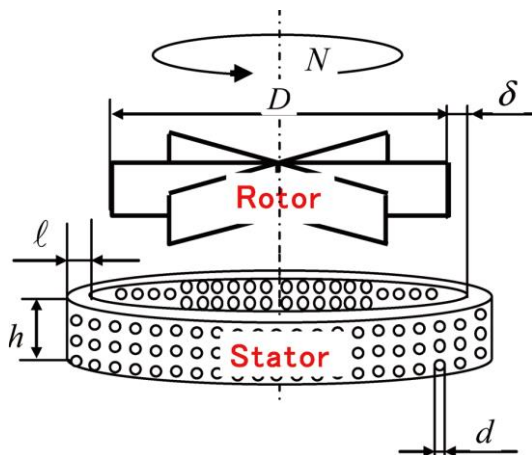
Dimensões do rotor e estator (retirado de Kamiya, T., et al 2010).
